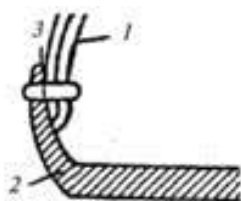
Бортовой метод: 1 – заготовка; 2 – подошва; 3 – кожаная лента
